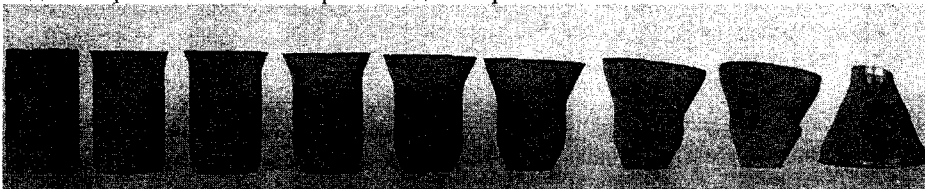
Формоизменение заготовки в штампе с обработкой поверхностей рабочего инструмента $Ra\ 3,2$
